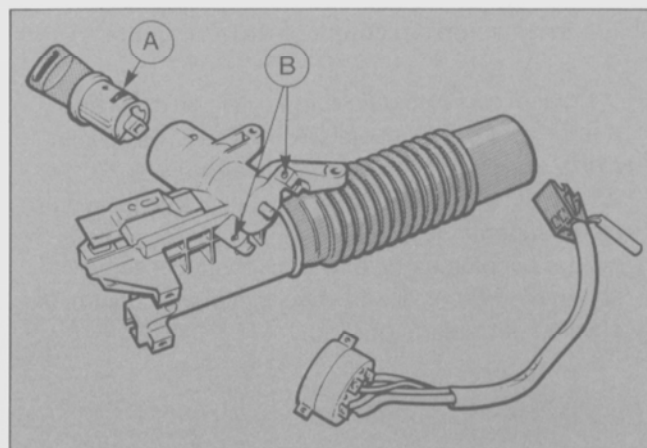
Interruptor y cilindro de la cerradura de la dirección.
